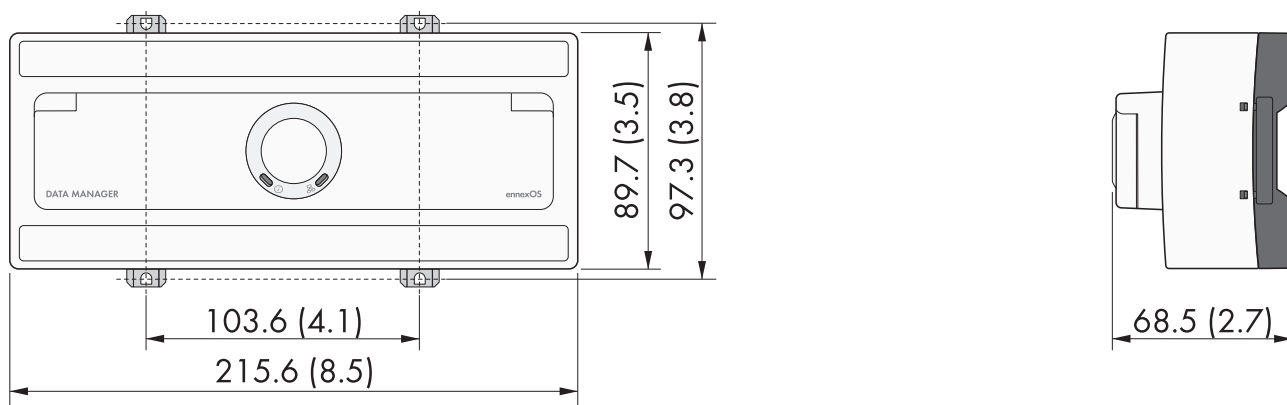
Dimensiones para el montaje en la pared (dimensiones en mm [in])
